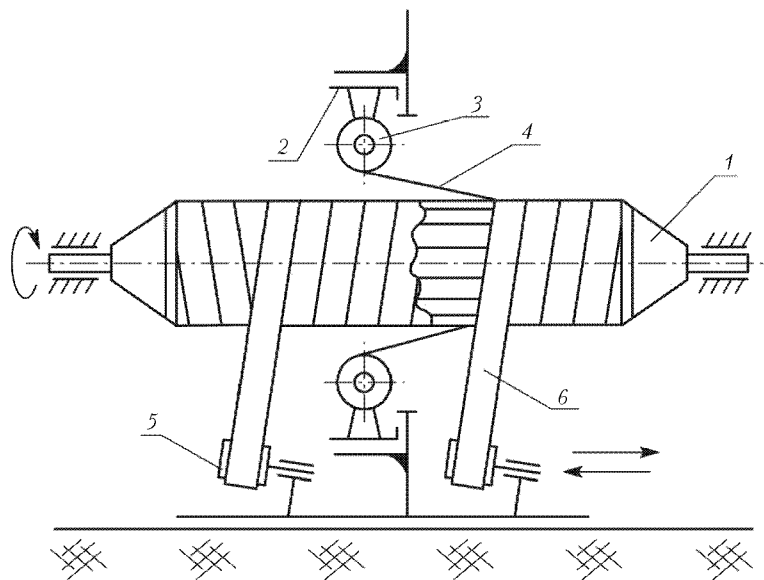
Схема продольно-поперечной намотки: 1 – оправка; 2 – вертлюг; 3 – шпули; 4 – ленты продольной укладки; 5 – поперечные раскладчики; 6 – ленты поперечной намотки
